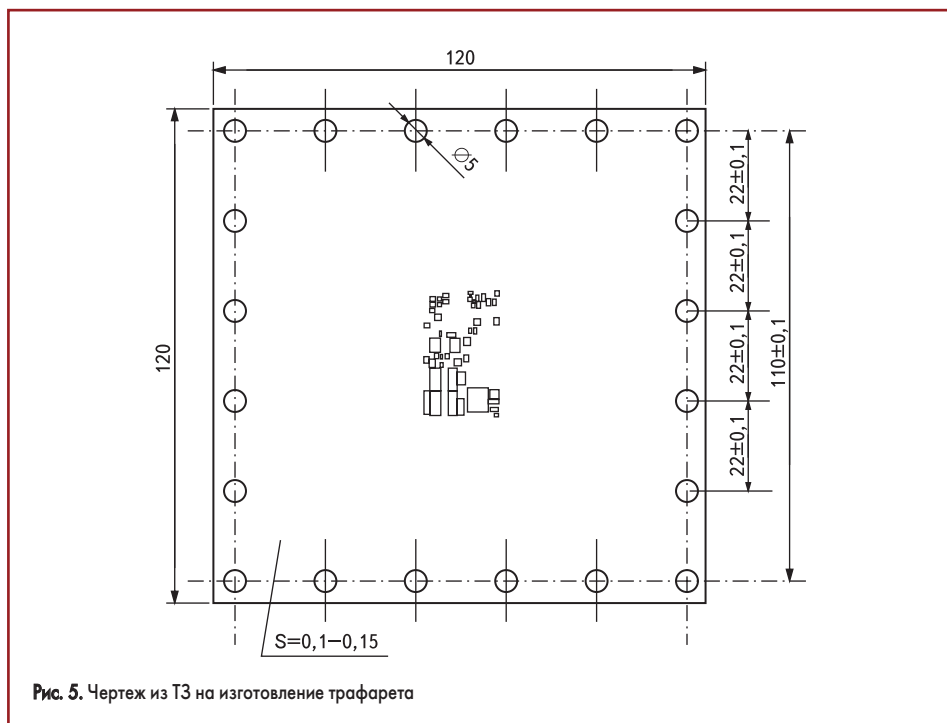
Чертеж из ТЗ на изготовление трафарета
